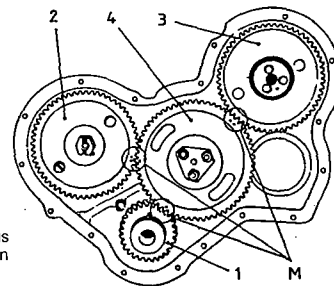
Conjunto de engranajes con sus marcas de puesta a punto respectivas en un motor de la marca PERKINS.
